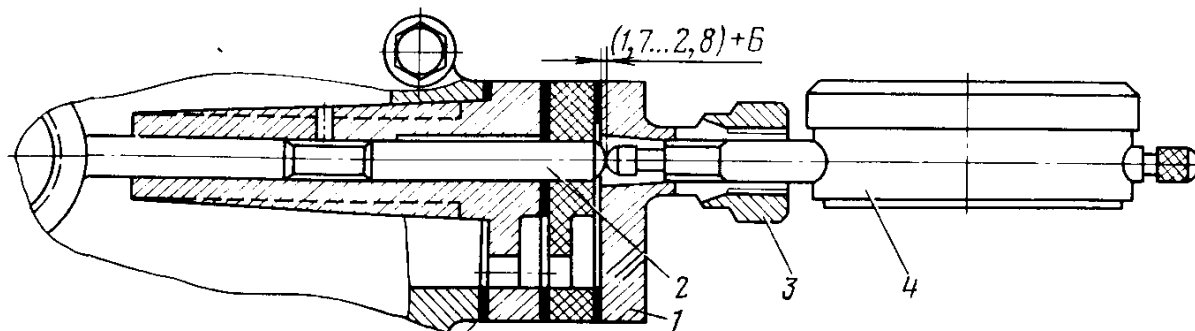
Приспособление для замера выступающего торца штанги привода топливного насоса: 1—фланец; 2—штанга; 3—гайка; 4—индикатор; Б—размер утопания рычага привода
